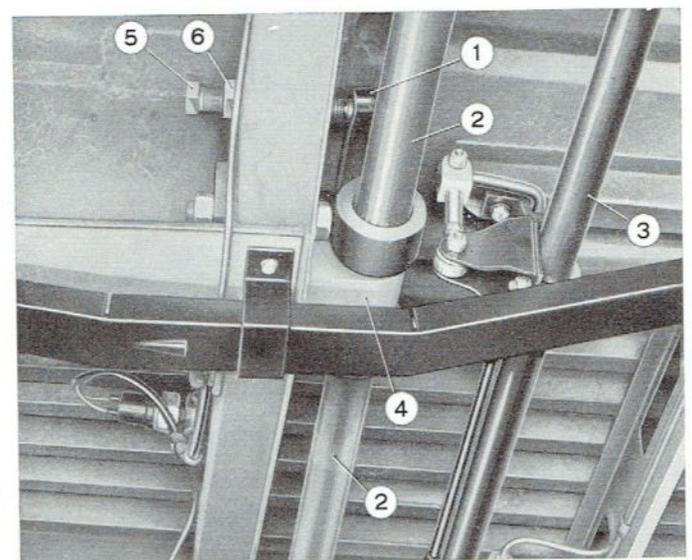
Detail des Lagerbocks in Fahrzeugmitte für Drehstabfeder.
